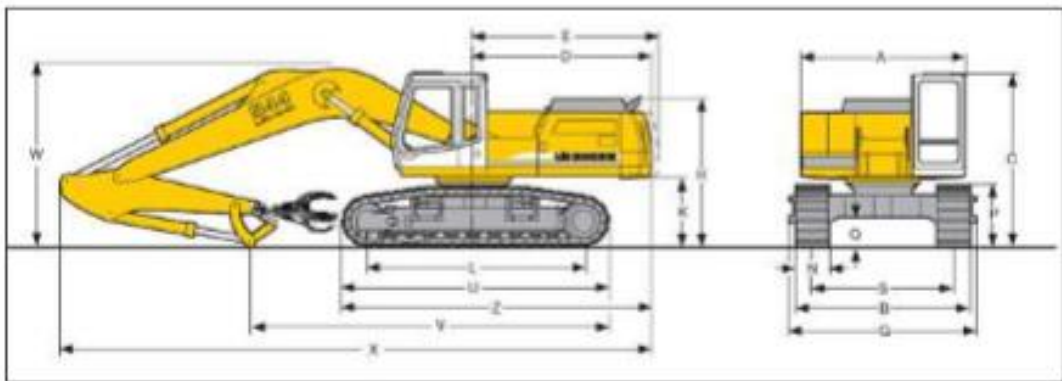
Dimensiones de Grúa LIEBHERR R944 (vista lateral y frontal)
